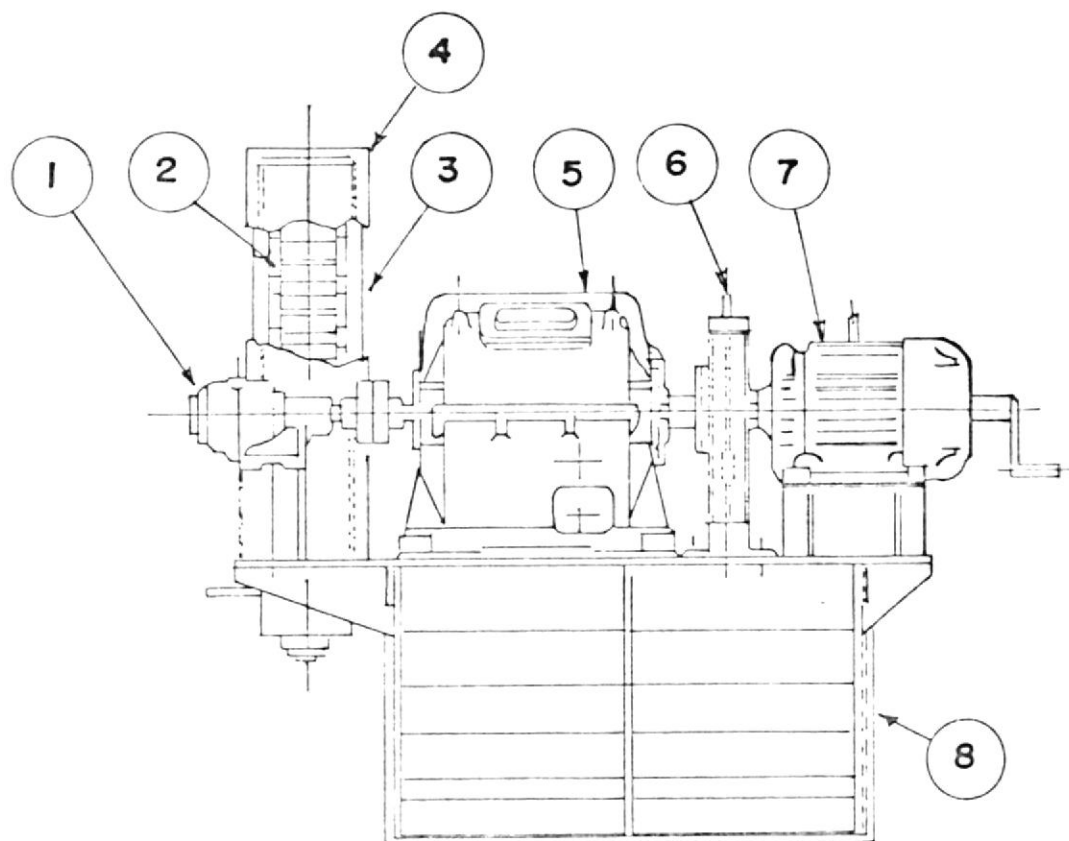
MONTAJE DE LA UNIDAD DEL ROTOR IMPULSOR
